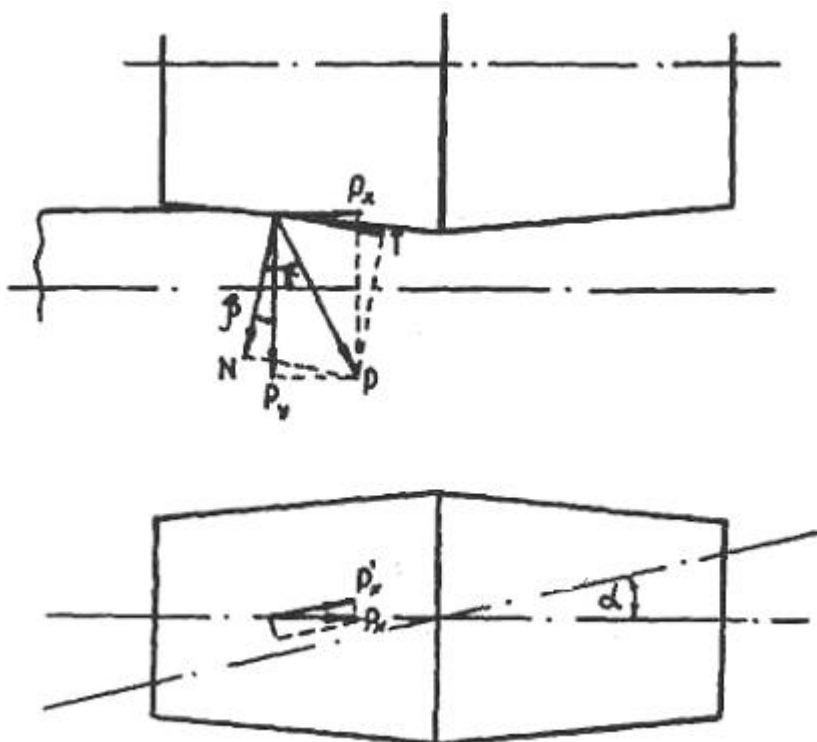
Схема сил, що діють в осередку деформації в момент захоплення заготовки валками вісь валку
